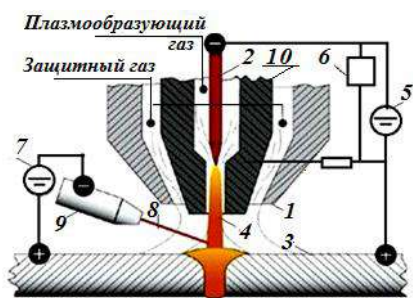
Сущность плазменно-дуговой сварки
